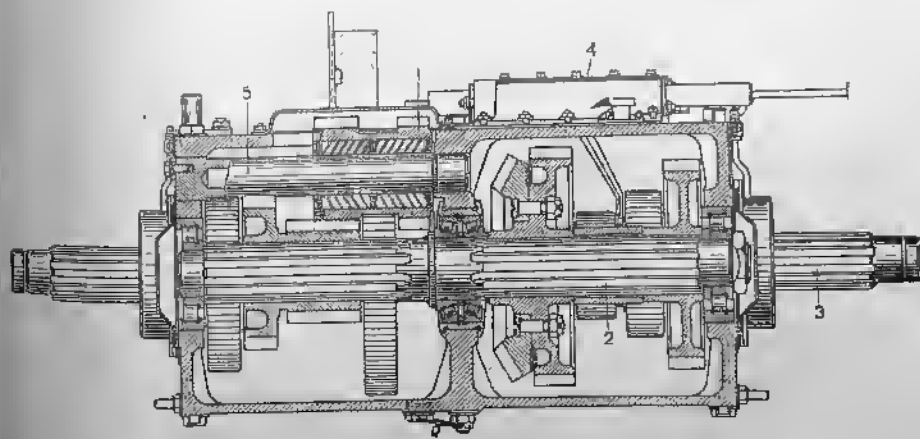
Четырехскоростная коробка передач (разрез по оси блока шестерен заднего хода и промежуточному валу):
